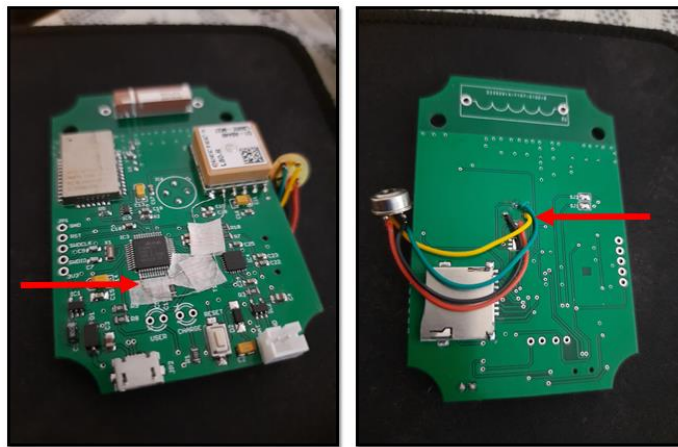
Primera versión PCB ensamblado. Fuente Autor.
